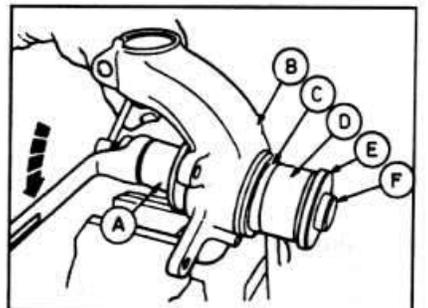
Применение специального инструмента для установки наружного кольца внешнего подшипника в поворотный кулак.
